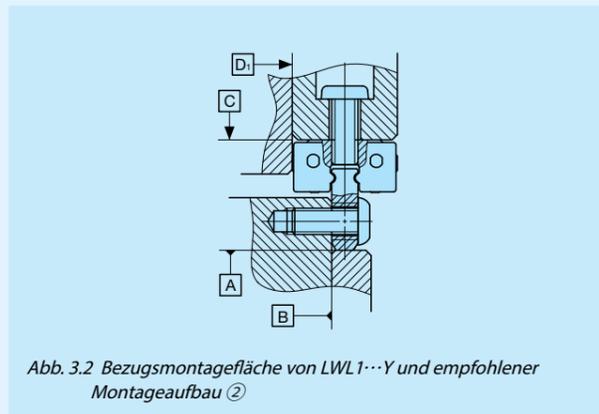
Bezugsmontagefläche von LWL1...Y und empfohlener Montageaufbau ②
